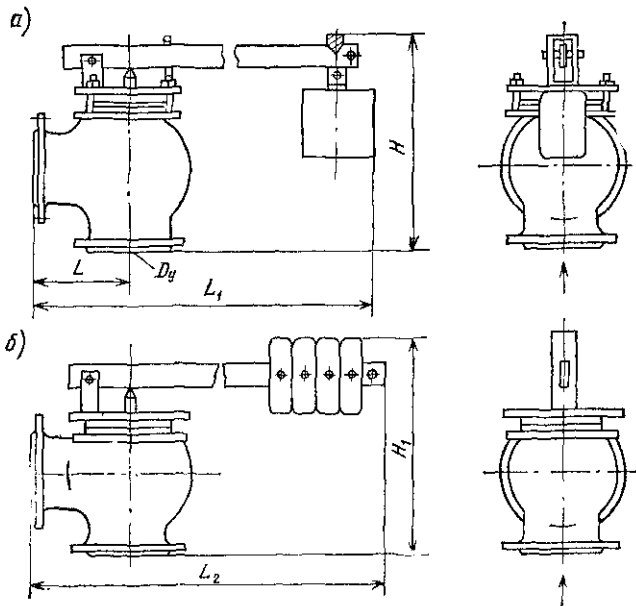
Клапан предохранительный рычажно-грузовой одинарный 17кч36р
